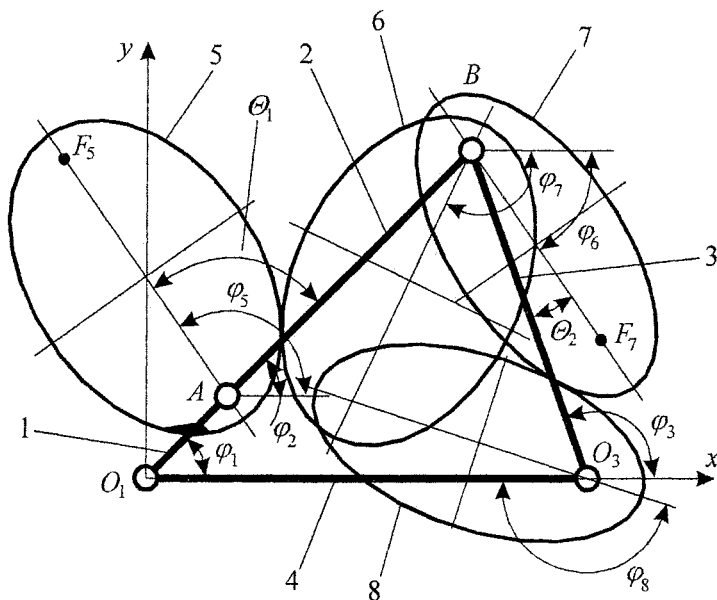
Схема зубчато-рычажного механизма с эллиптическими зубчатыми колесами
